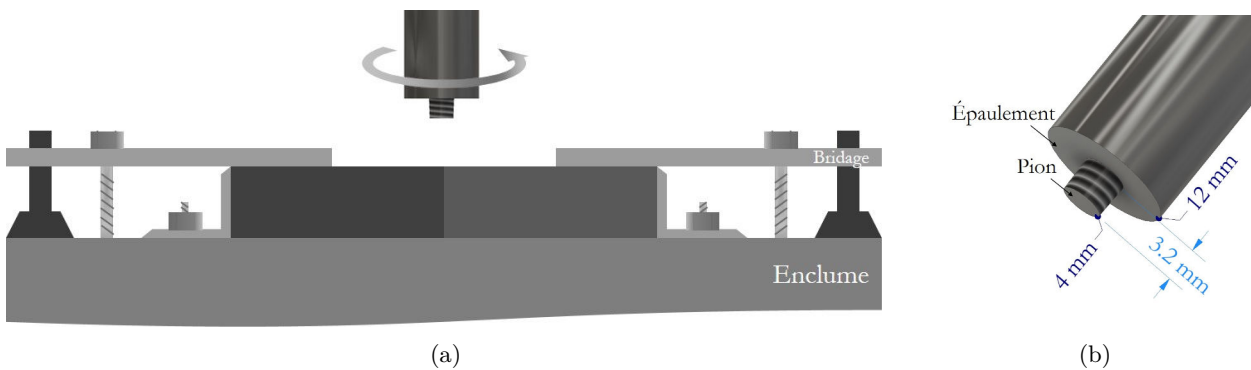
Schémas généraux de l'application de la soudure par friction malaxage. (a) Montage pour la mise en œuvre du FSW. (b) Outil FSW avec un pion conique fileté et un épaulement plat.
